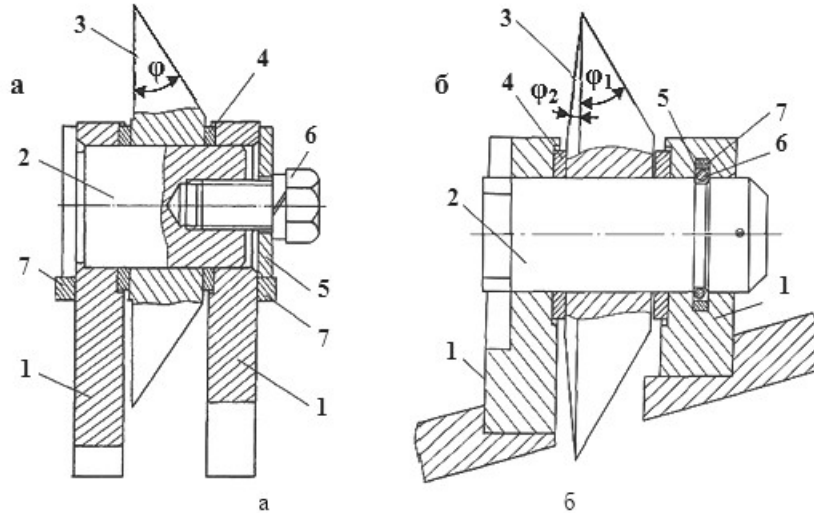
Конструкции узлов крепления дисковых инструментов:
